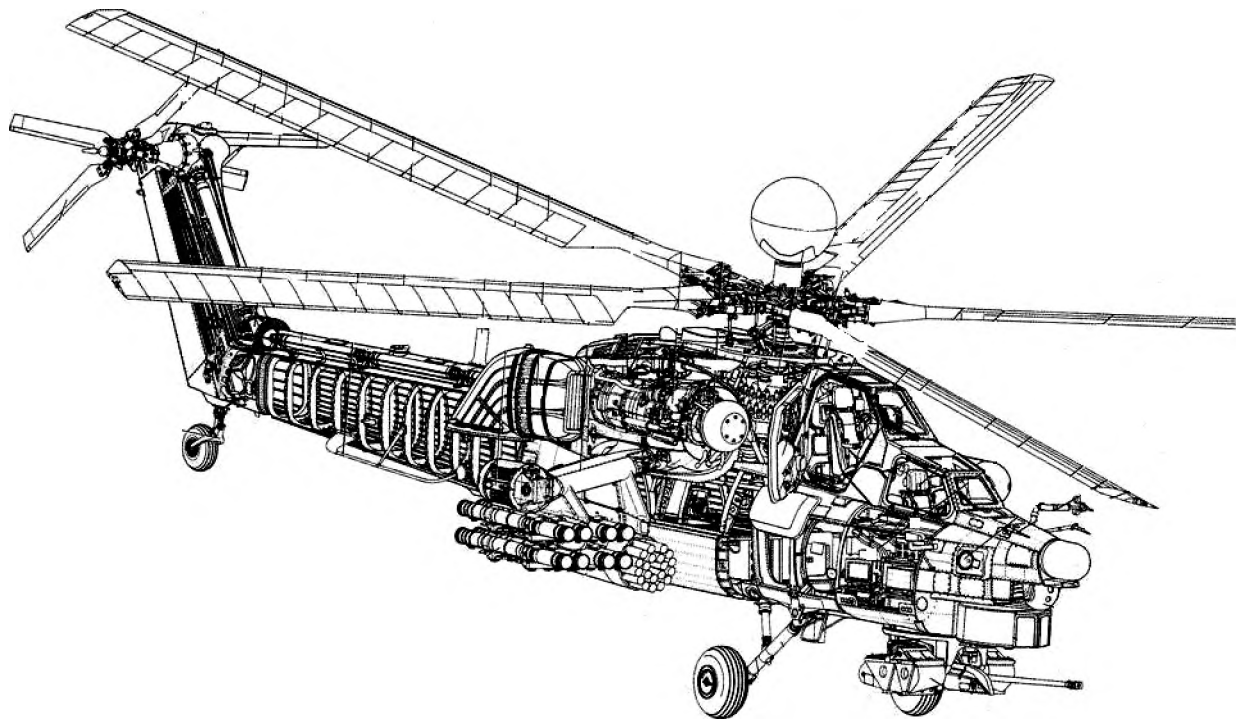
Конструкция балочно-рычажного шасси и рычага вертолета Ми-28 [14]:
